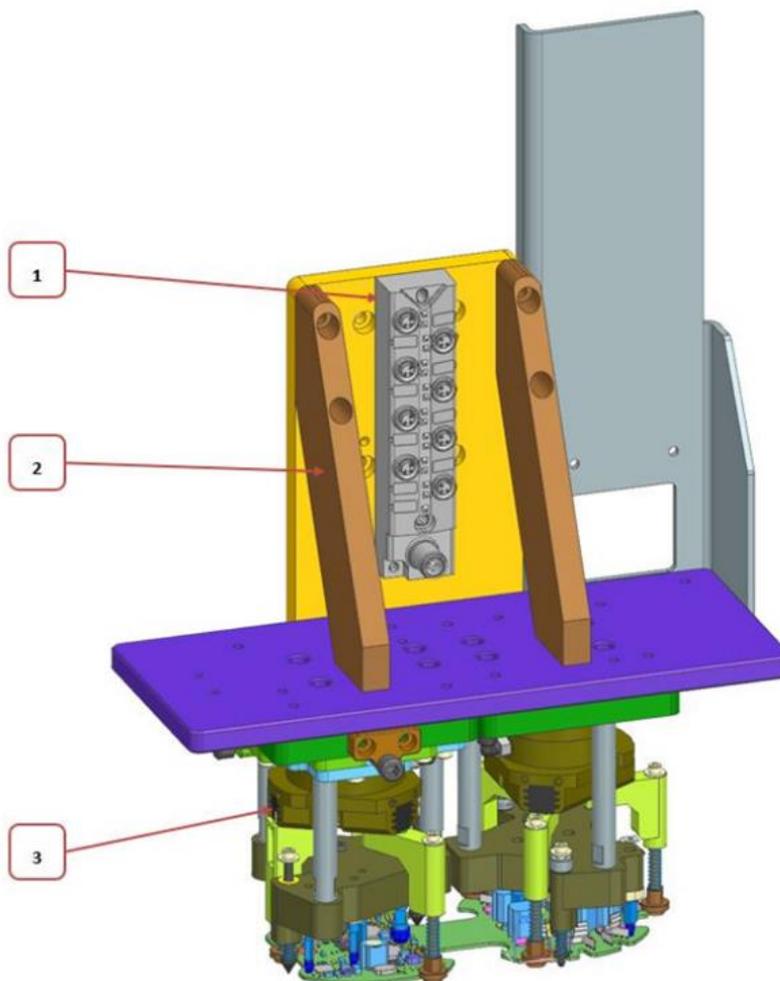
3D CAD модель головки захвату з монтажними пластинами: 1 - розподільна коробка; 2 – опора; 3 - захват
